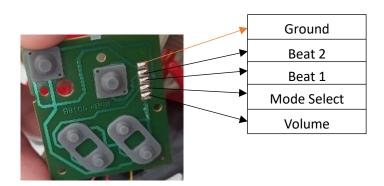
Locais para soldadura de fios na placa 1
